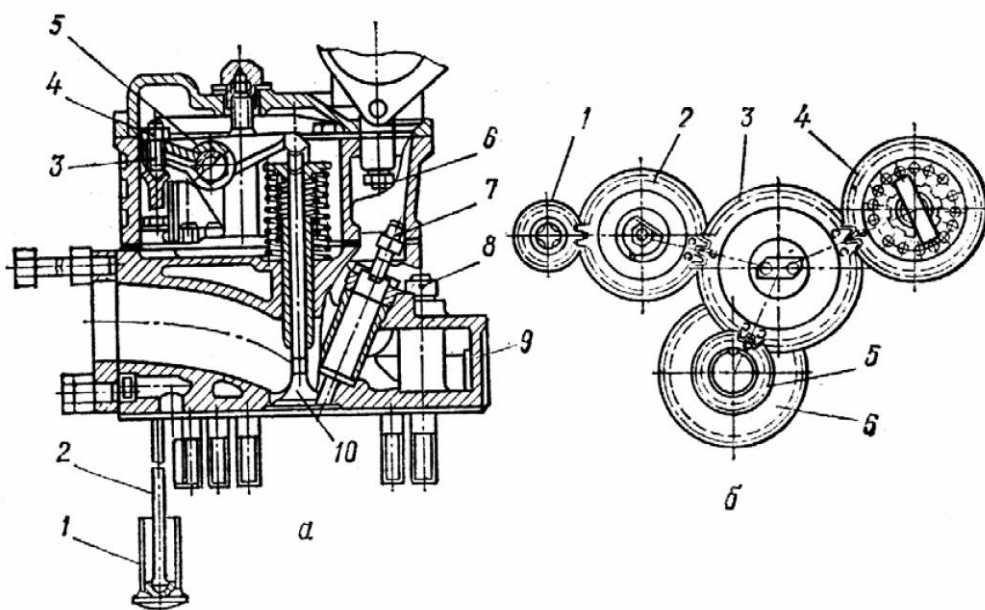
Газораспределительный механизм двигателя Д-240: а - механизм газораспределения двигателя Д-240: 1 - толкатель; 2 - штанга; 3 - регулировочный винт; 4 - гайка регулировочного винта; 5 - коромысло; 5 - шпилька крепления впускного коллектора; 7 - шпилька крепления форсунки; 8 - гайка стакана форсунки; 9 - стакан форсунки; 10 - впускной клапан; б - установка шестерен газораспределения двигателя Д-240: 1 - шестерня привода насоса НШ-10У; 2 - шестерня распределительного вала; 3 - промежуточная шестерня; 4 - шестерня привода топливного насоса; 5 - шестерня коленчатого вала; 6 - шестерня привода масляного насоса
